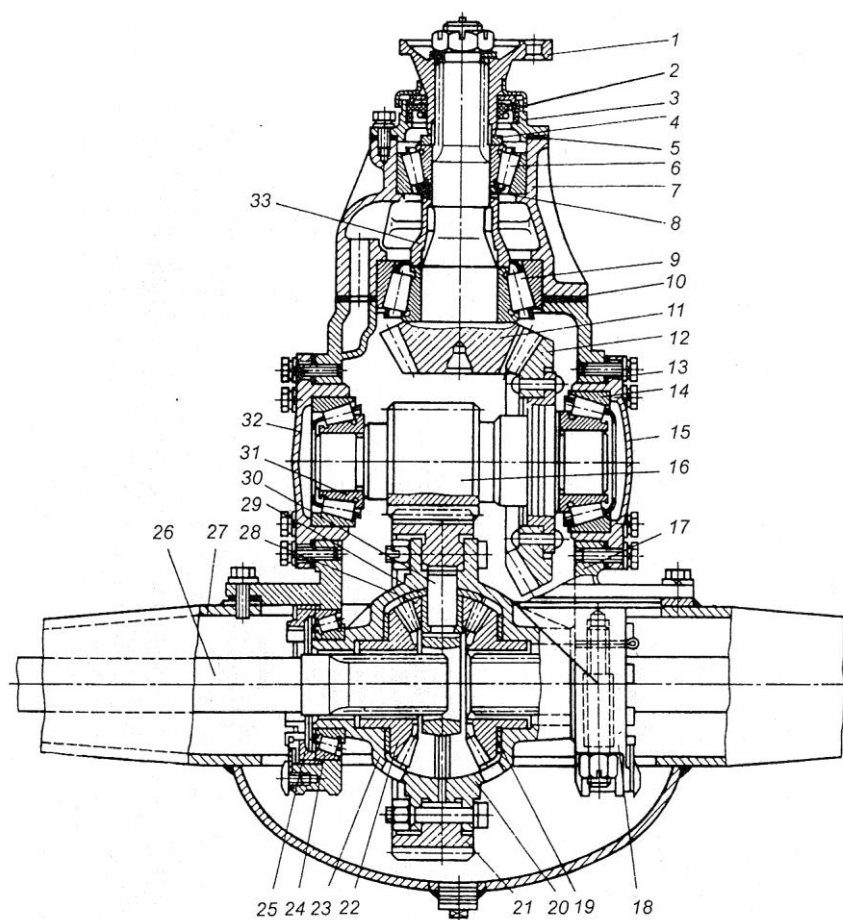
Главная двойная передача с дифференциалом: 1 – фланец; 2 – манжета; 3,15,18,32 – крышки; 4 – шайба; 5 – уплотнительная прокладка; 6,9,14,24,31 – роликоподшипники; 7 – стакан; 8 – регулировочные шайбы; 10,13 – регулировочные прокладки; 11 – ведущее коническое зубчатое колесо; 12 – ведомое коническое зубчатое колесо; 16,21 – цилиндрические зубчатые колеса; 17 – картер главной передачи; 19,29 – опорные шайбы; 20 – правая чашка дифференциала; 22 – полуосевая шестерня; 23 – левая чашка дифференциала; 25 – регулировочная гайка; 26 – полуось; 27 – картер моста; 28 – сателлит; 30 – крестовина; 33 – распорная втулка
